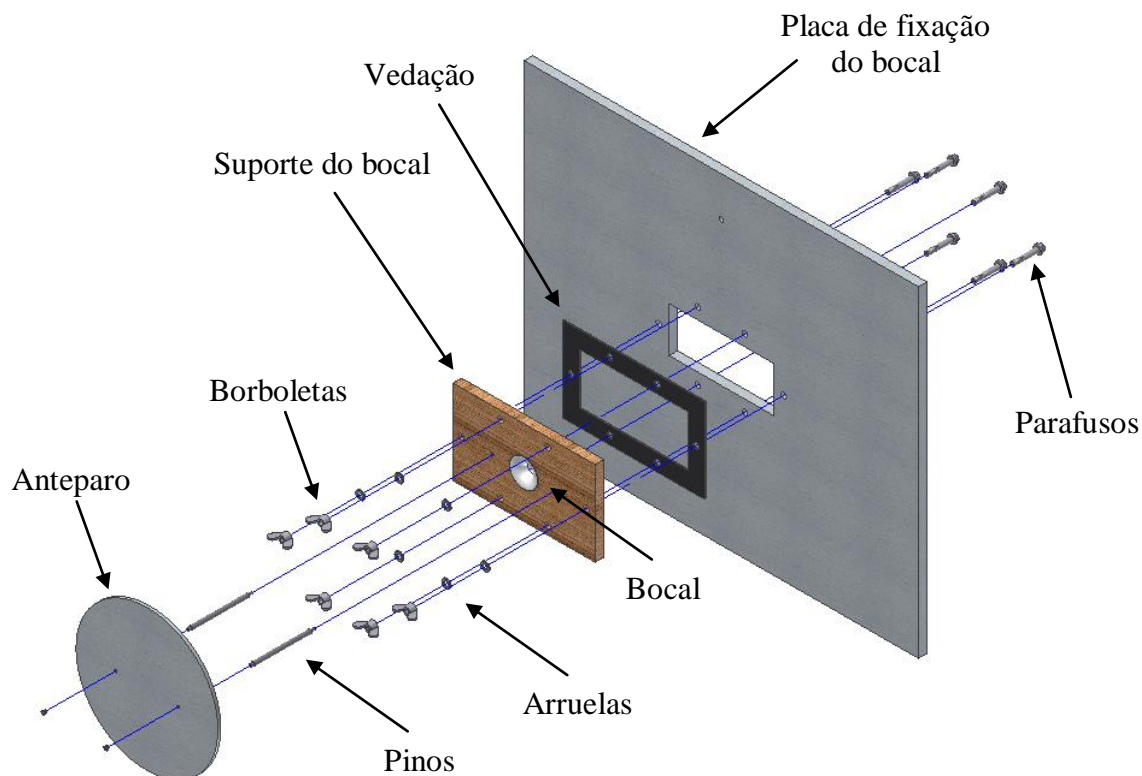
Vista explodida da placa de fixação do bocal.
